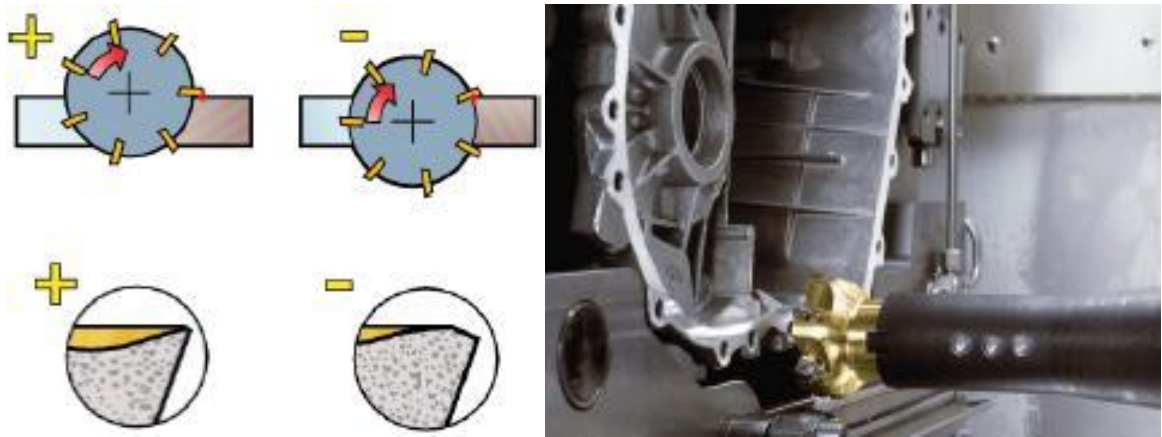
Контурна обробка торцевими фрезами тонкостінних деталей
